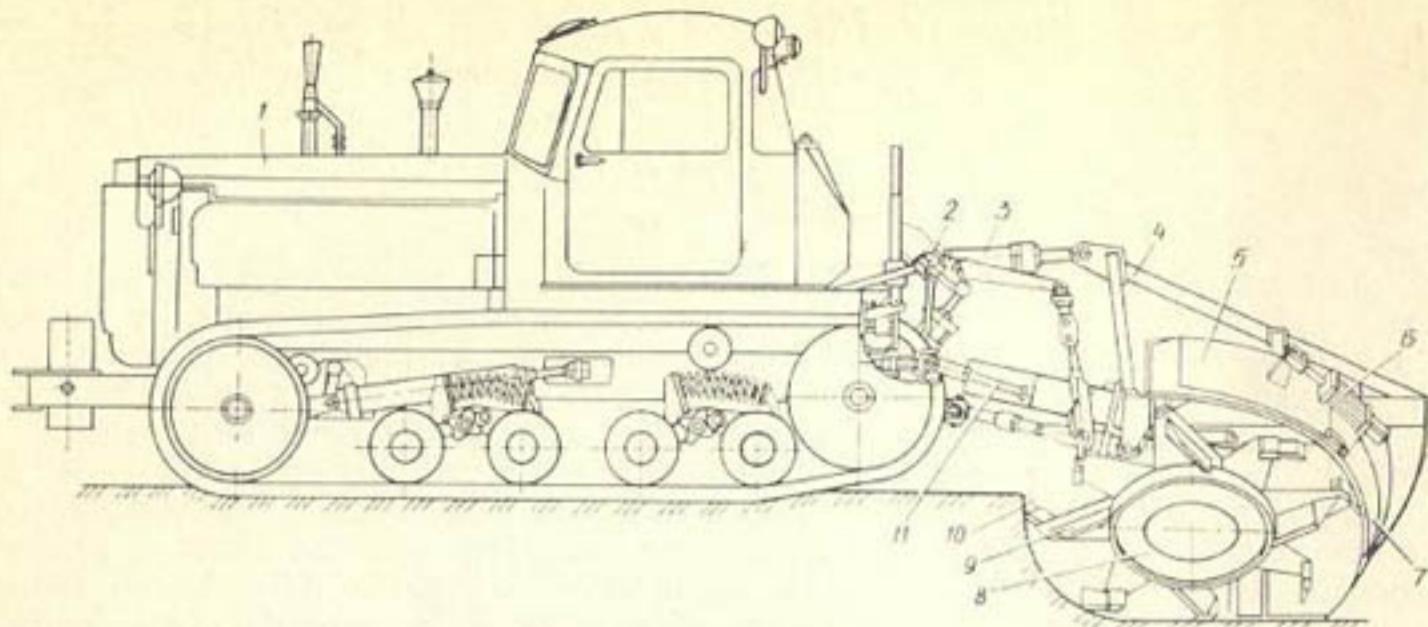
Схема плужно-роторного каналокопателя МК-17:
